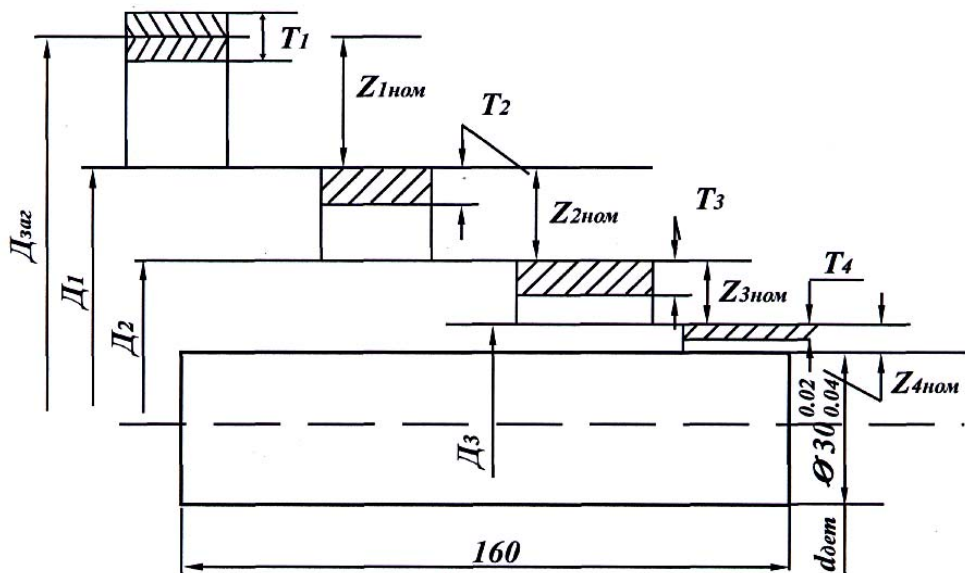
Схема розташування операційних розмірів припусків і допусків.
